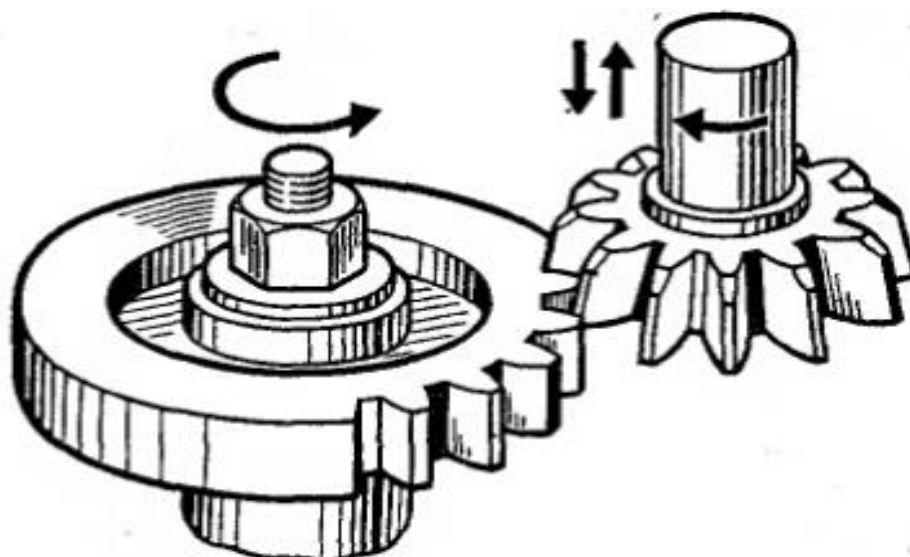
Схема зубодолбления на зубодолбёжном станке:
